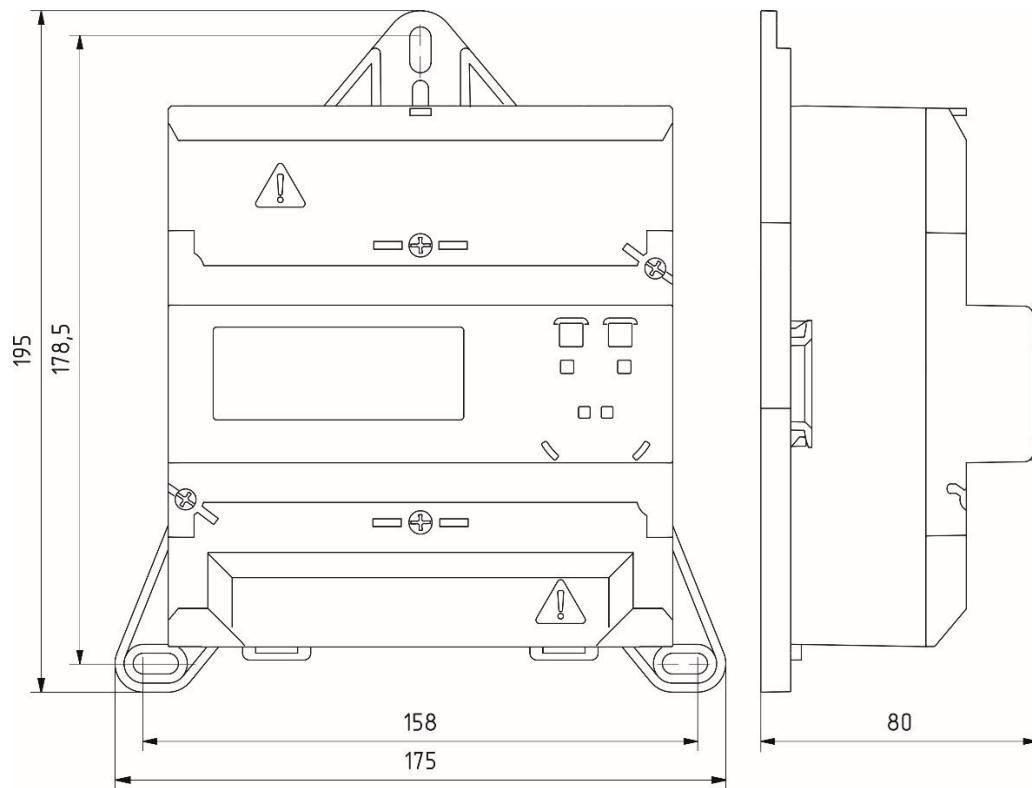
Тип корпуса D37, крепление на кронштейн
